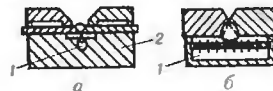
Схеми газових подушок: а, б — одно- і двобічне зварювання; 1 — захисний газ; 2 — відли підкладка
